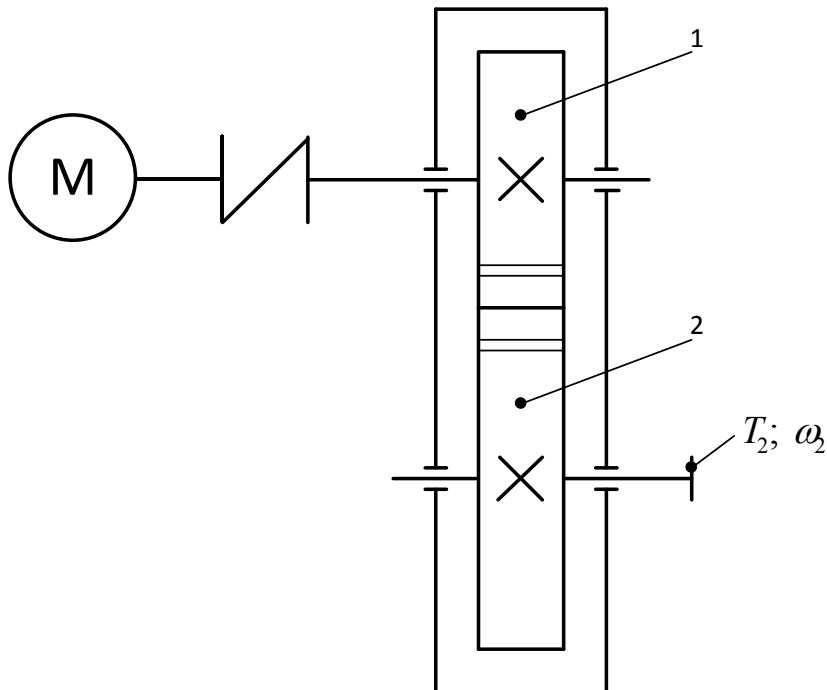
Схема закритої прямозубої циліндричної передачі
